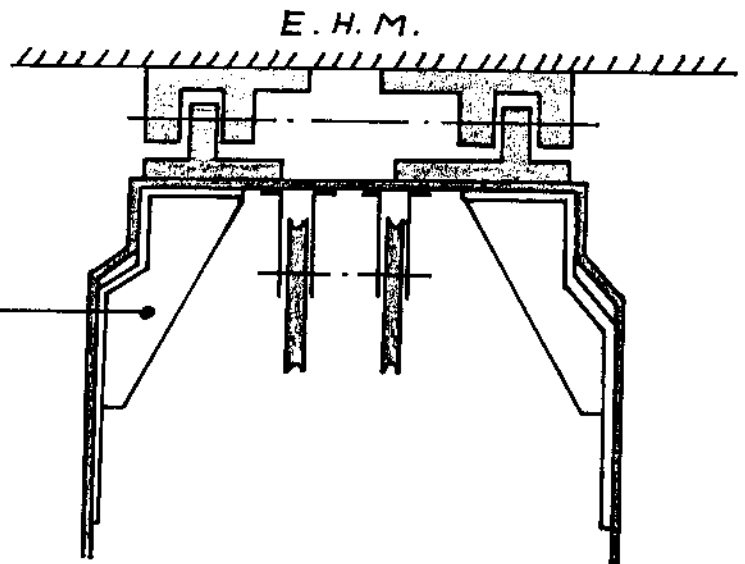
Vue en coupe de la poutre Fuselage sous E.H.M.
